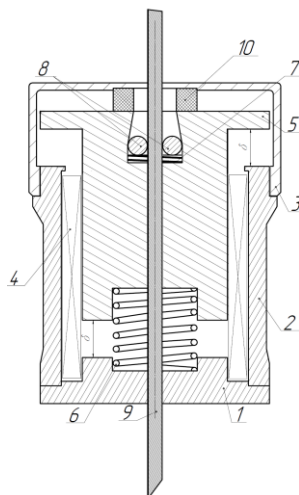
Линейный шаговый электромагнитный двигатель
